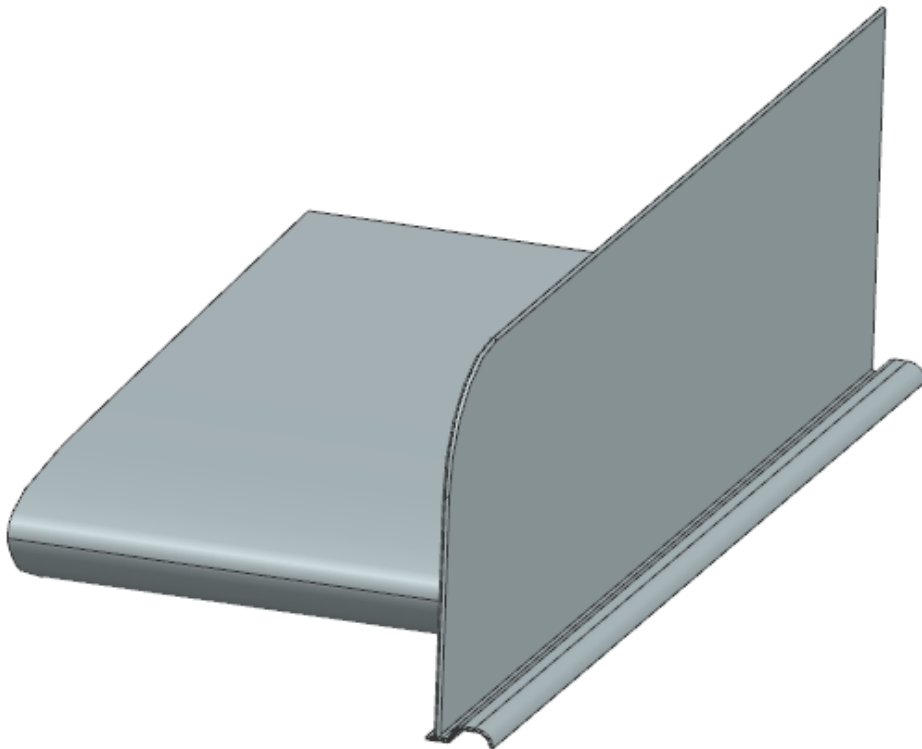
Vista prospettica dell'ENDPLATE 1
